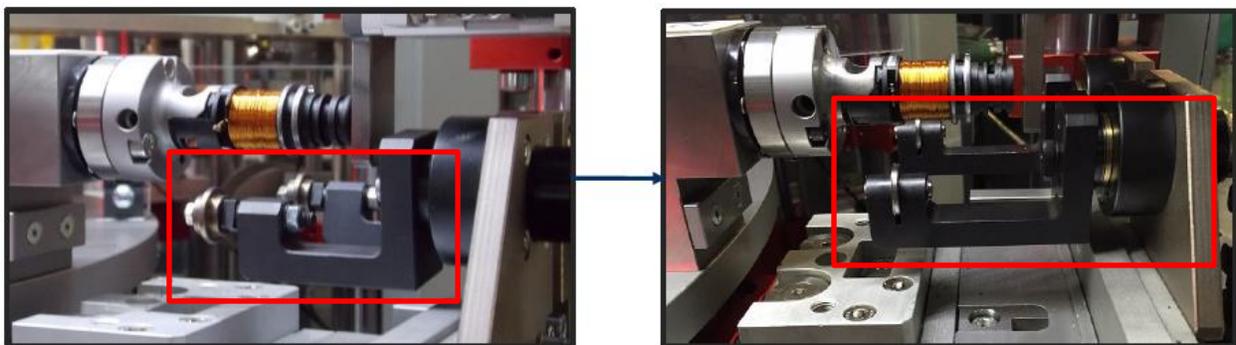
Brazo mecánico anterior y brazo mecánico actual.
